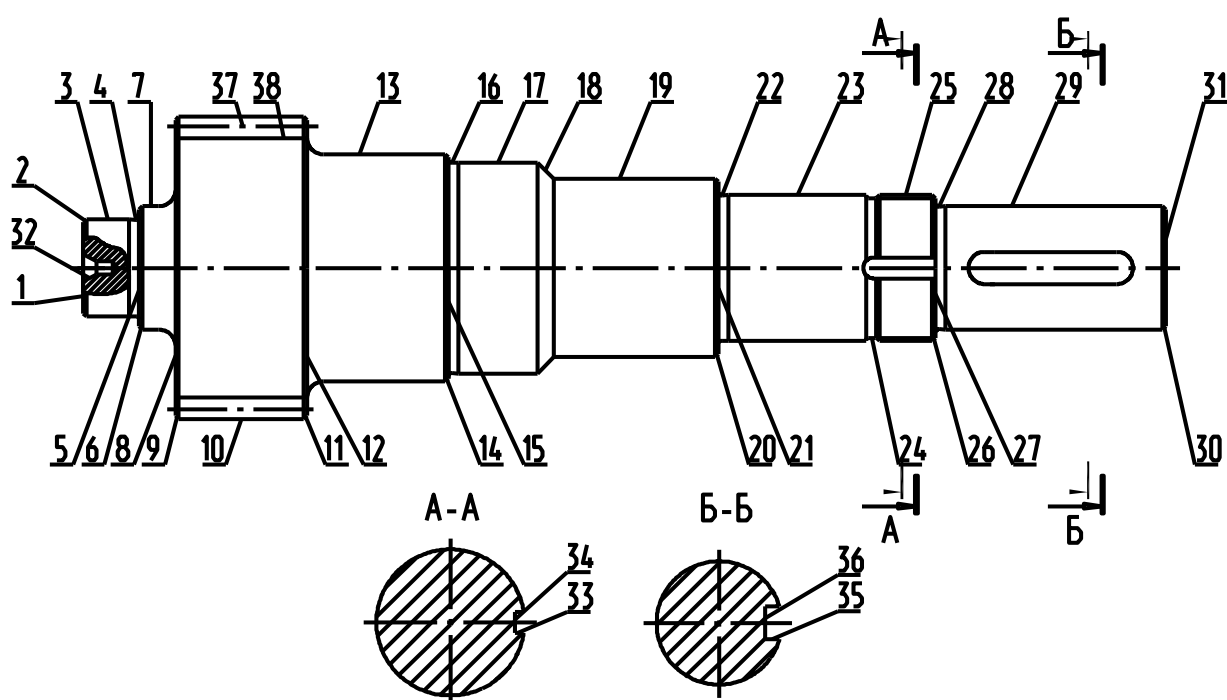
Общий вид вала-шестерни с обозначением поверхностей
